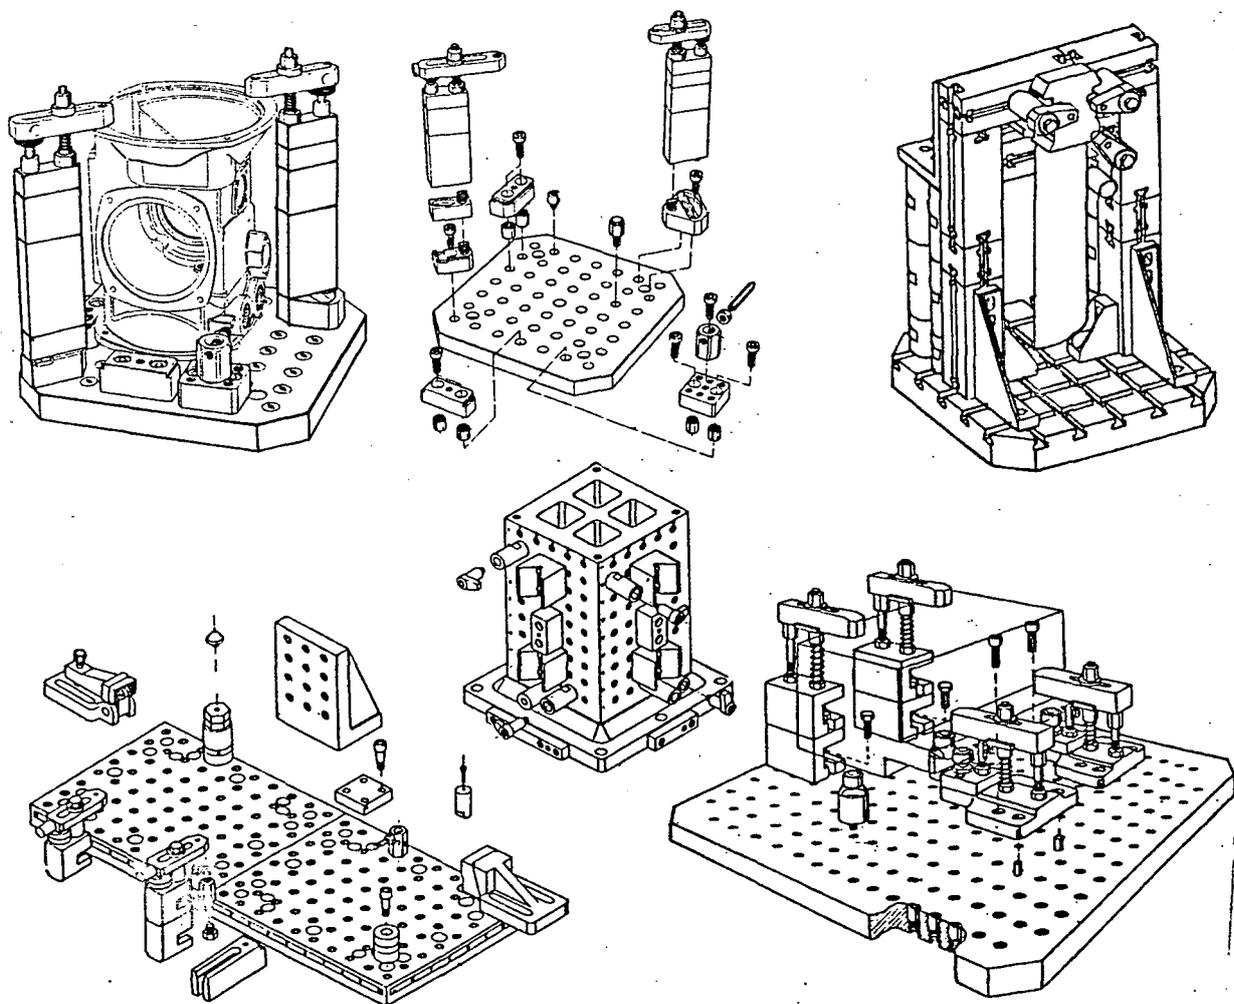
Exemplos de conjuntos modulares de dispositivos de fixação para usinagem de peças [16 e 21].
